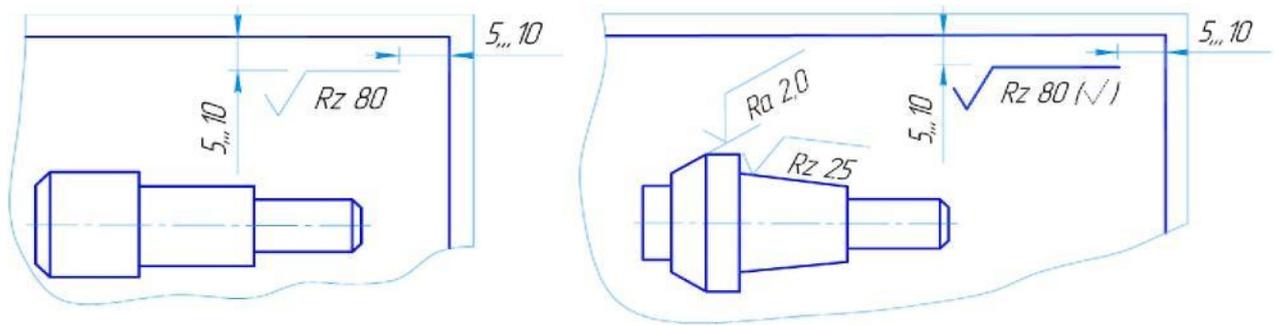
Обозначение одинаковых шероховатостей Рис. 10. Обозначение преобладающей шероховатости
